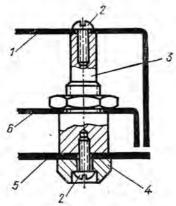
Способ скрепления панелей корпуса и шасси: 1 — верхняя паиель; 2 - винты  $M2,5 \times 6; 3 -$  стойка, сталь Ст 3. цинковать; 4 — ножка, сталь Ст 3, хромировать или воронить: 5 - нижняя панель; 6maccu.
